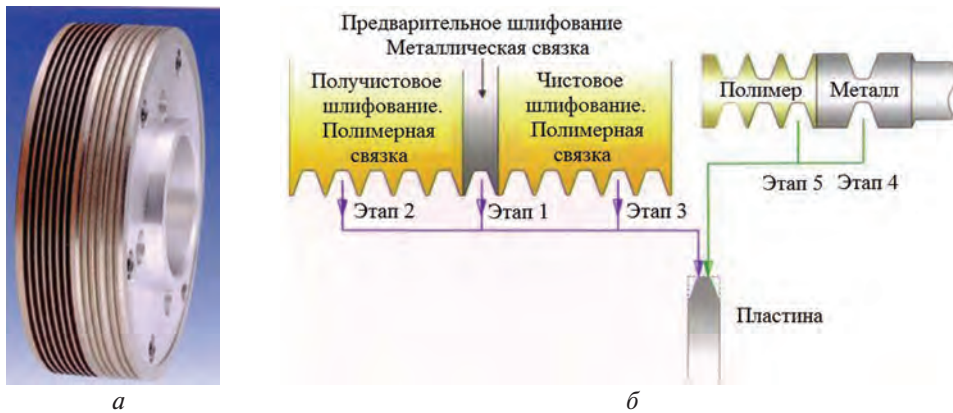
Многосекционный инструмент для обработки фасок кремниевых пластин: *a* — компоновка инструмента; *б* — этапы шлифовки и полировки фаски
